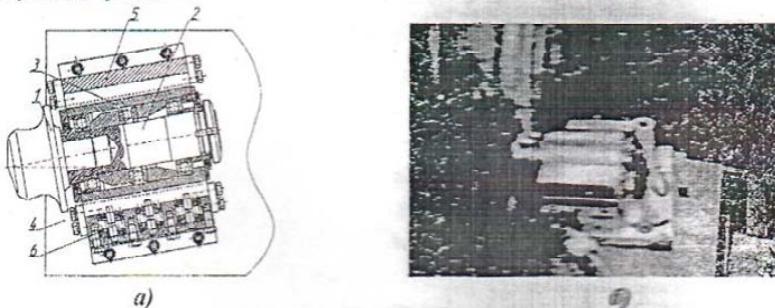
Конструкція розкочувальної головки (а) і загальний вигляд розкочувальної приставки до лобового токарного верстата (б)
